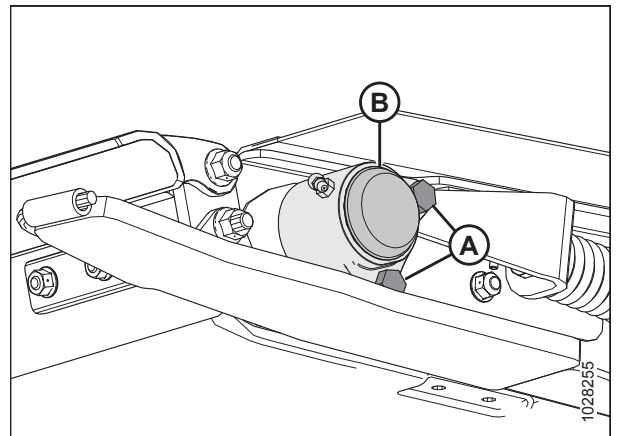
Rodamiento de rodillo tensor: lado izquierdo
